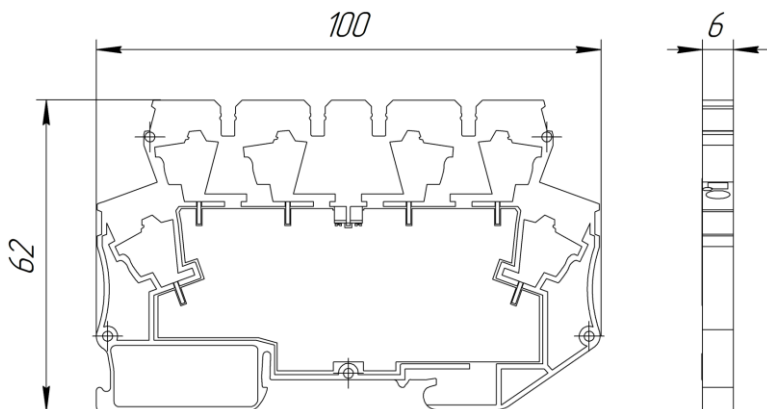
Габаритный чертеж модулей NLS-1R12, NLS-1R24 без боковой крышки
